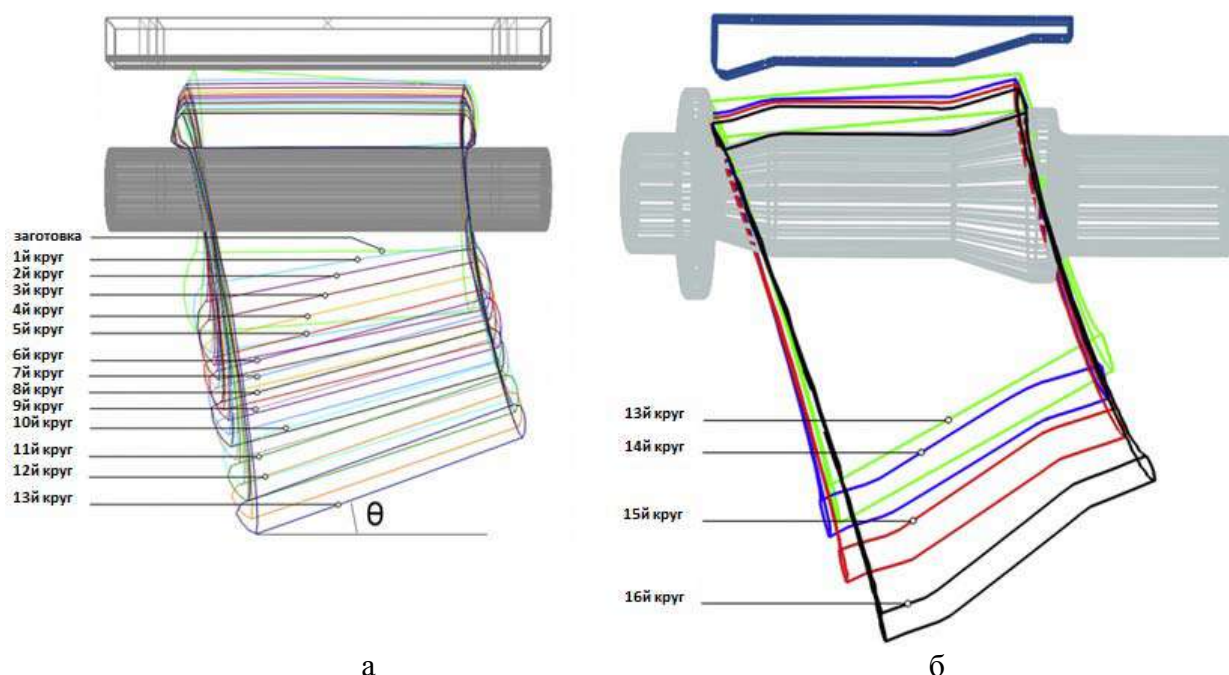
Получение заготовки (а) и окончательнаяковка (б) изготовления конической обечайки с двумя цилиндрическими прямыми участками
